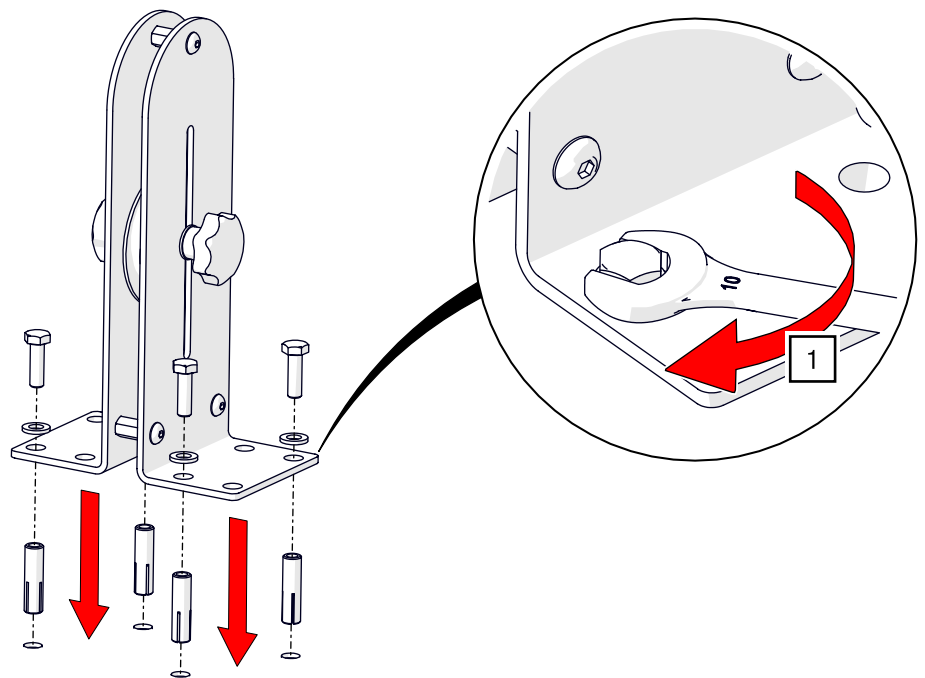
Gegenspannrolle mit dem Boden verschrauben
